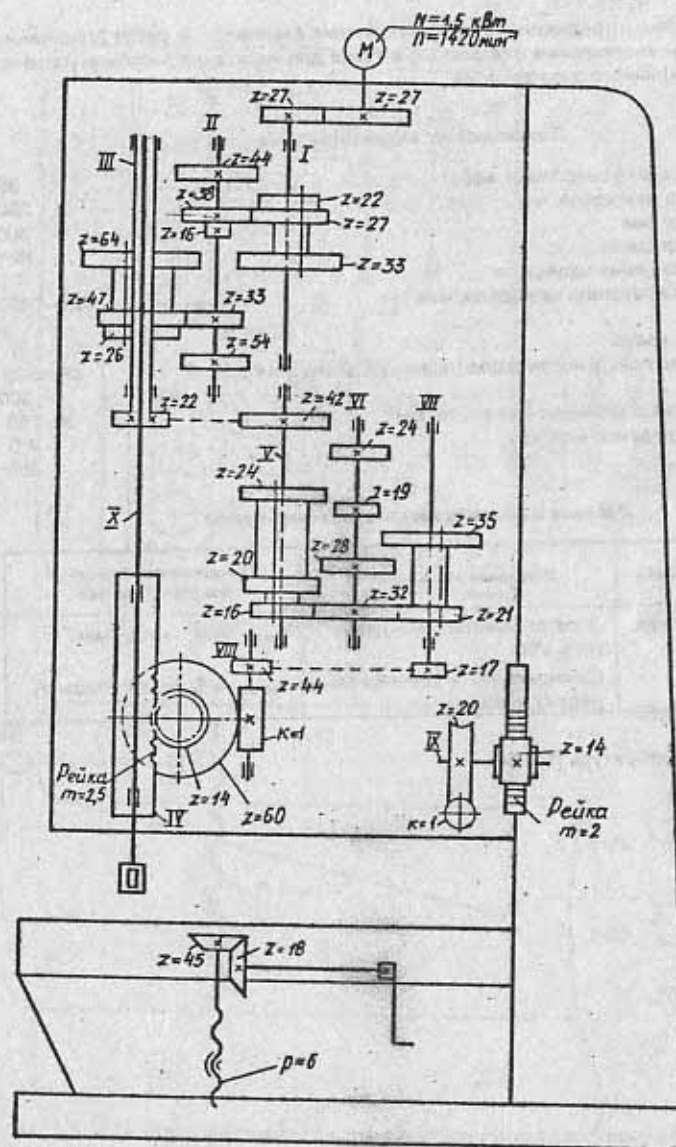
Кинематическая схема вертикально-сверлильного станка мод. 2Н118
